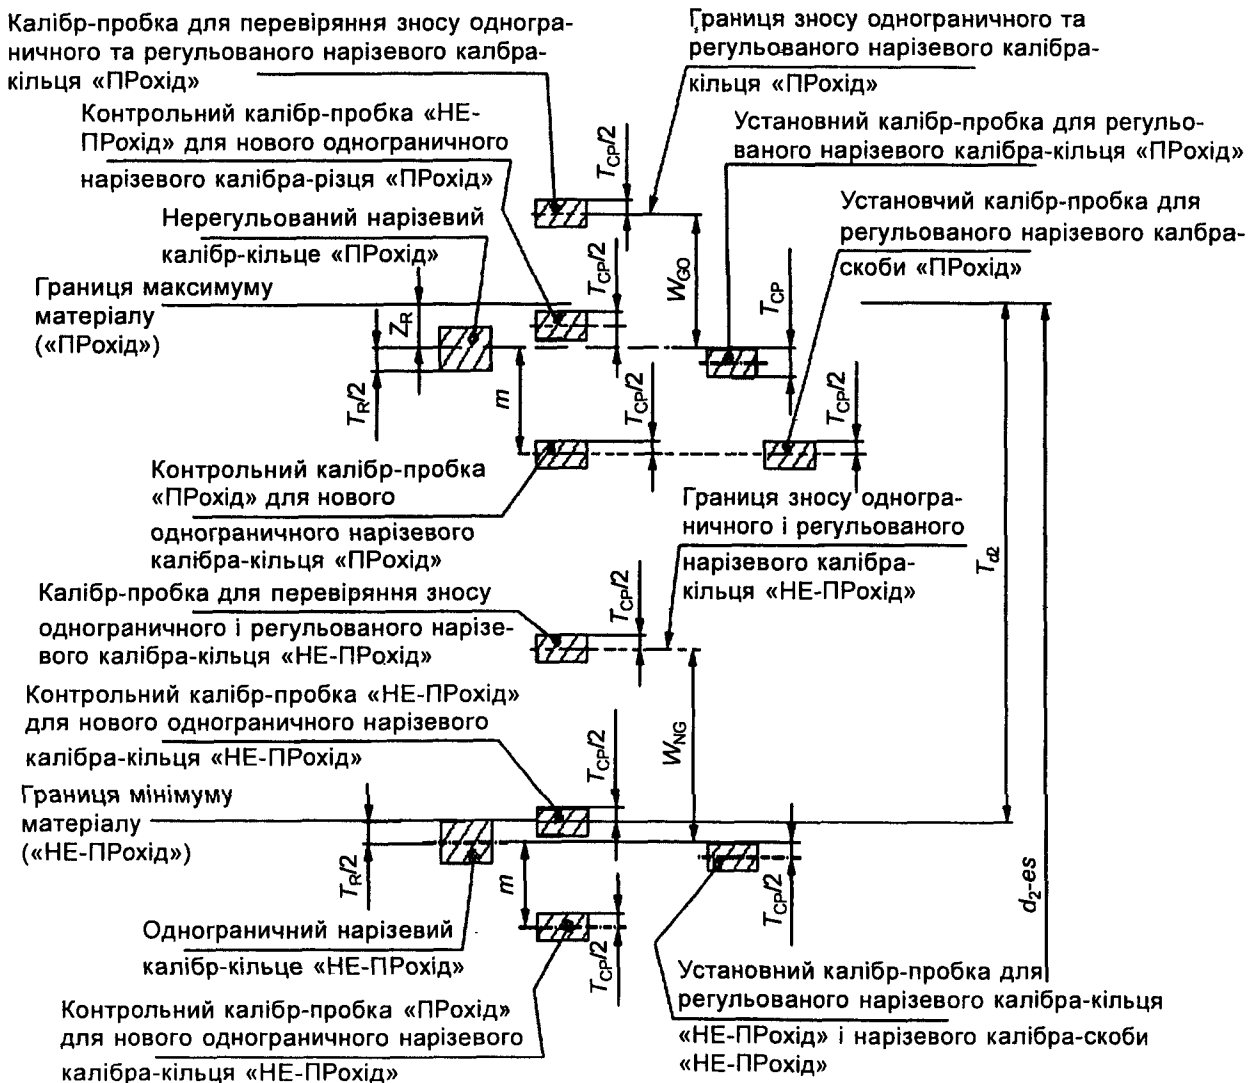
Поля допусків середнього діаметра калібрів для контролювання зовнішньої нарізі (схема розташування)
